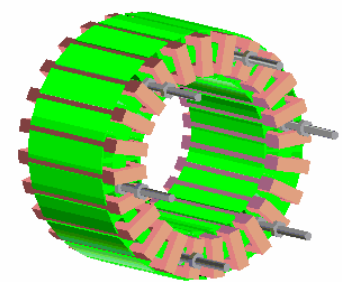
Bobinage Gramme pour machine à flux radial [QU 03]
